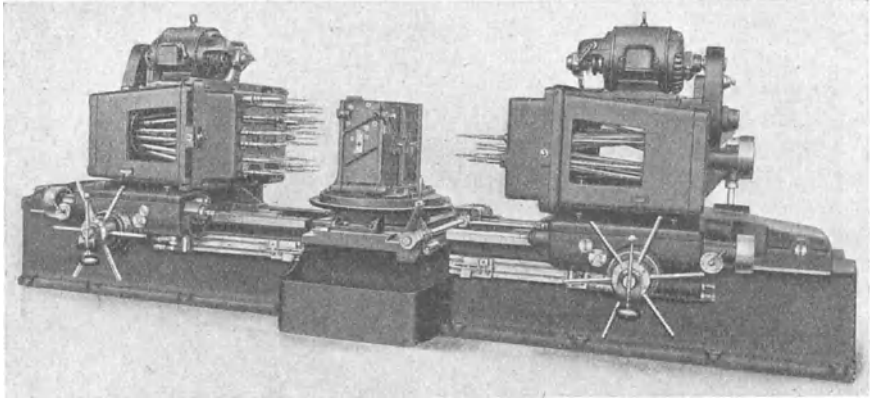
Mehrspindlige Waagrechtbohrmaschine. (Habersang & Zinzen G. m. b. H., Düsseldorf-Oberbilk.)
